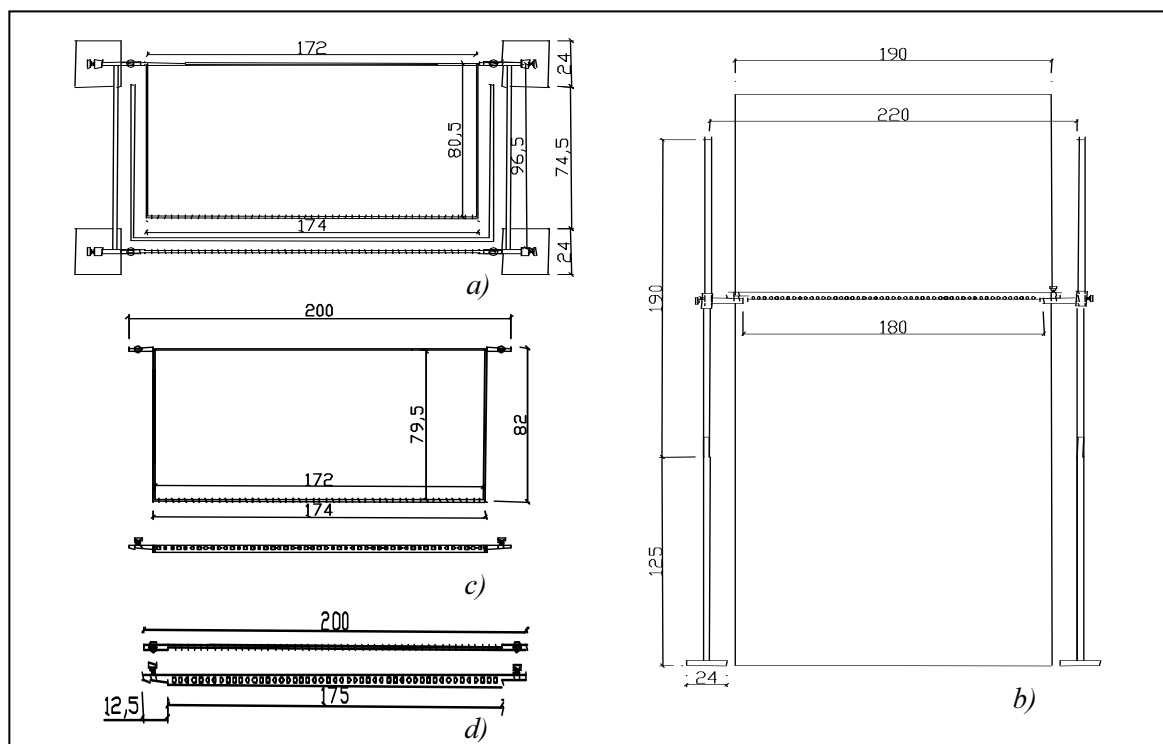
Accessorio costruito per le misure spettrofotometriche in situ: a) pianta; b) prospetto; c) pianta e prospetto dell'asta orizzontale da posizionare sul fronte dell'accessorio; d) pianta e prospetto dell'asta orizzontale da posizionare sul retro dell'accessorio (quote in cm).
